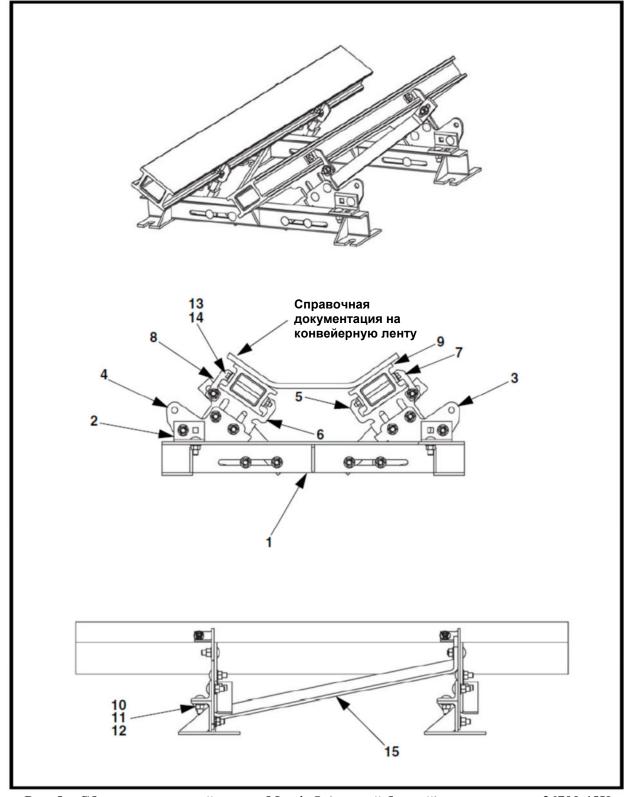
а. Сборка скользящей опоры Martin® (с одной балкой), номер детали 36700-18X
